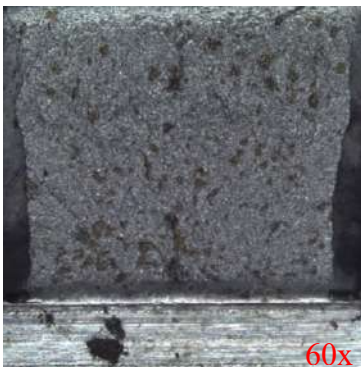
Vista macroscópica de la fractura 22MnB5, -40°C, condición 3.
